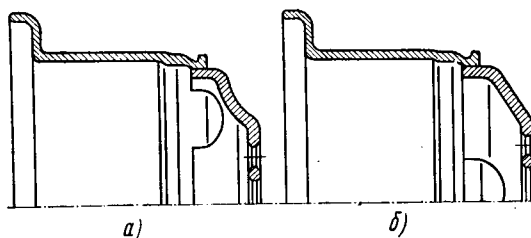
Конструкция соединений нераскатанных дисков с ободьями колес: а — 7,0—20; б — 7,5В—20
